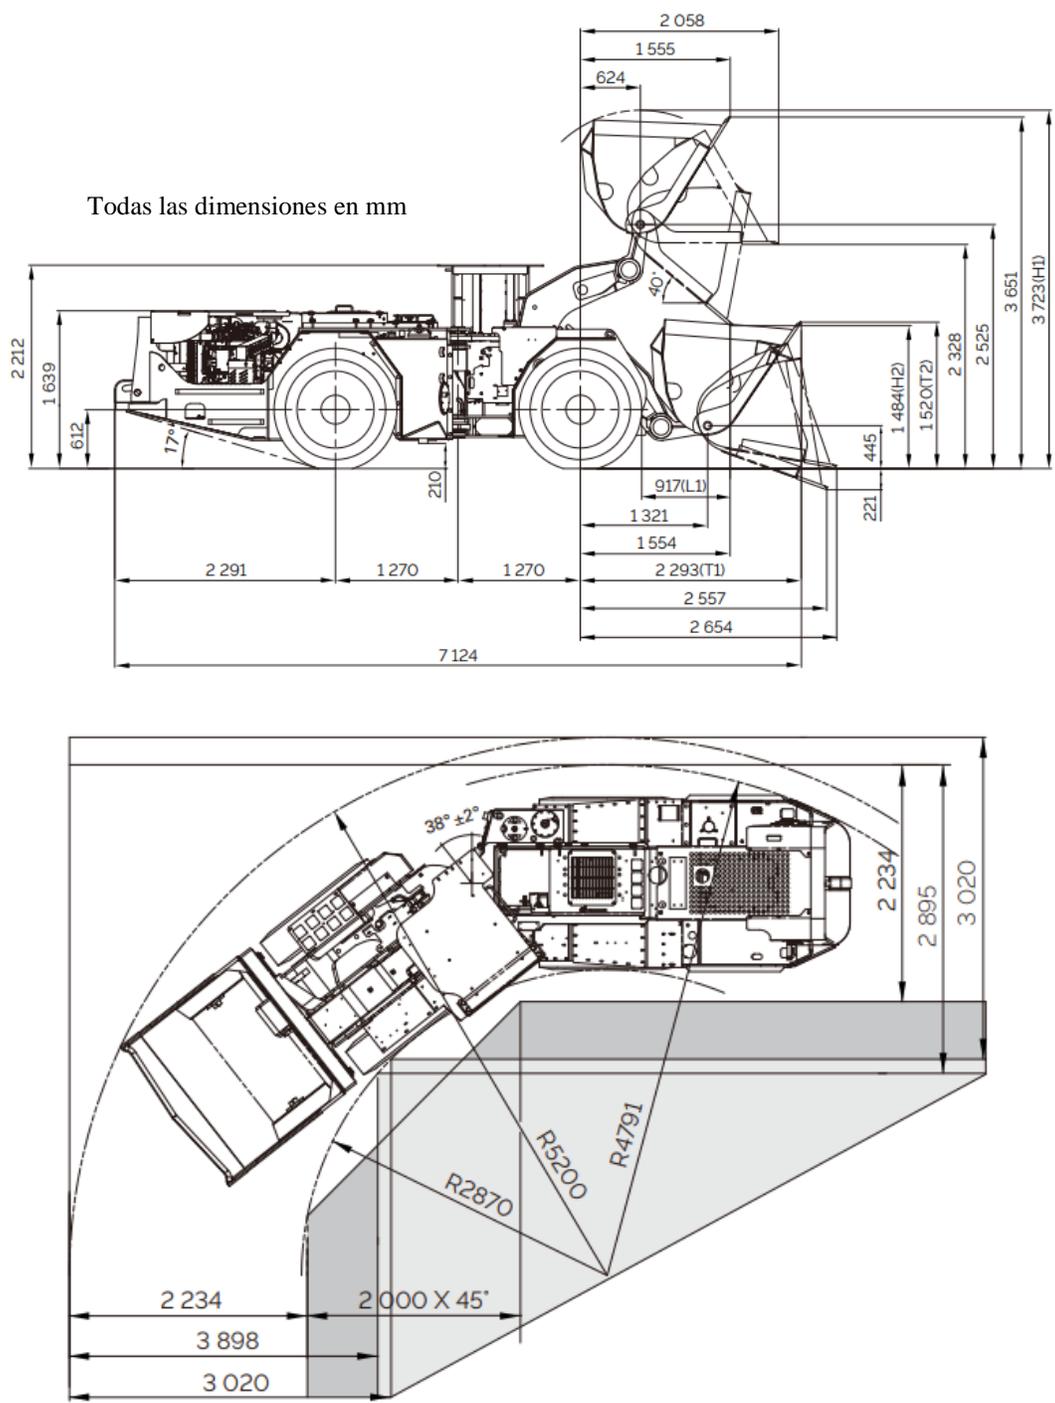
Dimensiones cargador ST2G. Fuente. Epiroc
